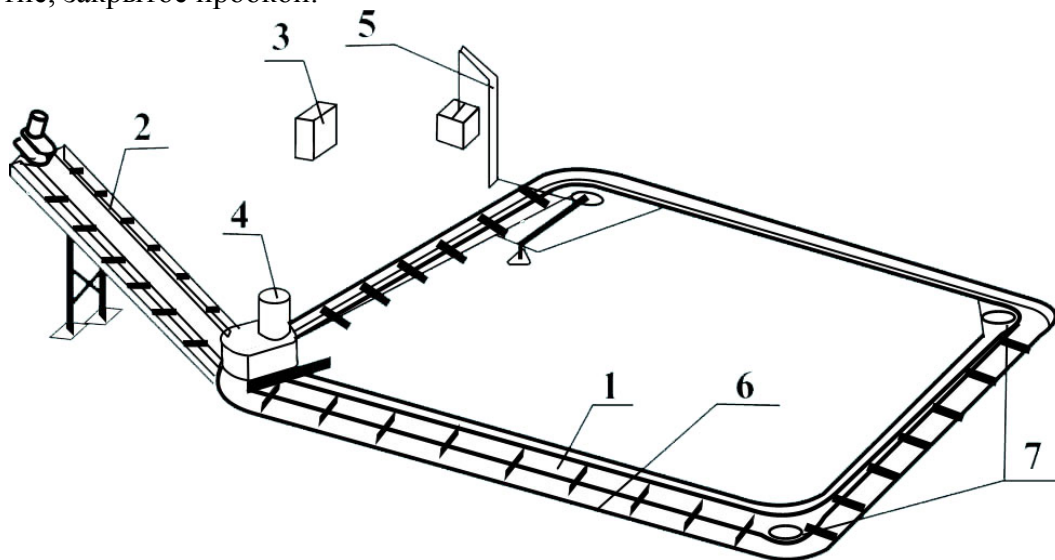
Транспортер скребковый навозоуборочный ТСН-160:
